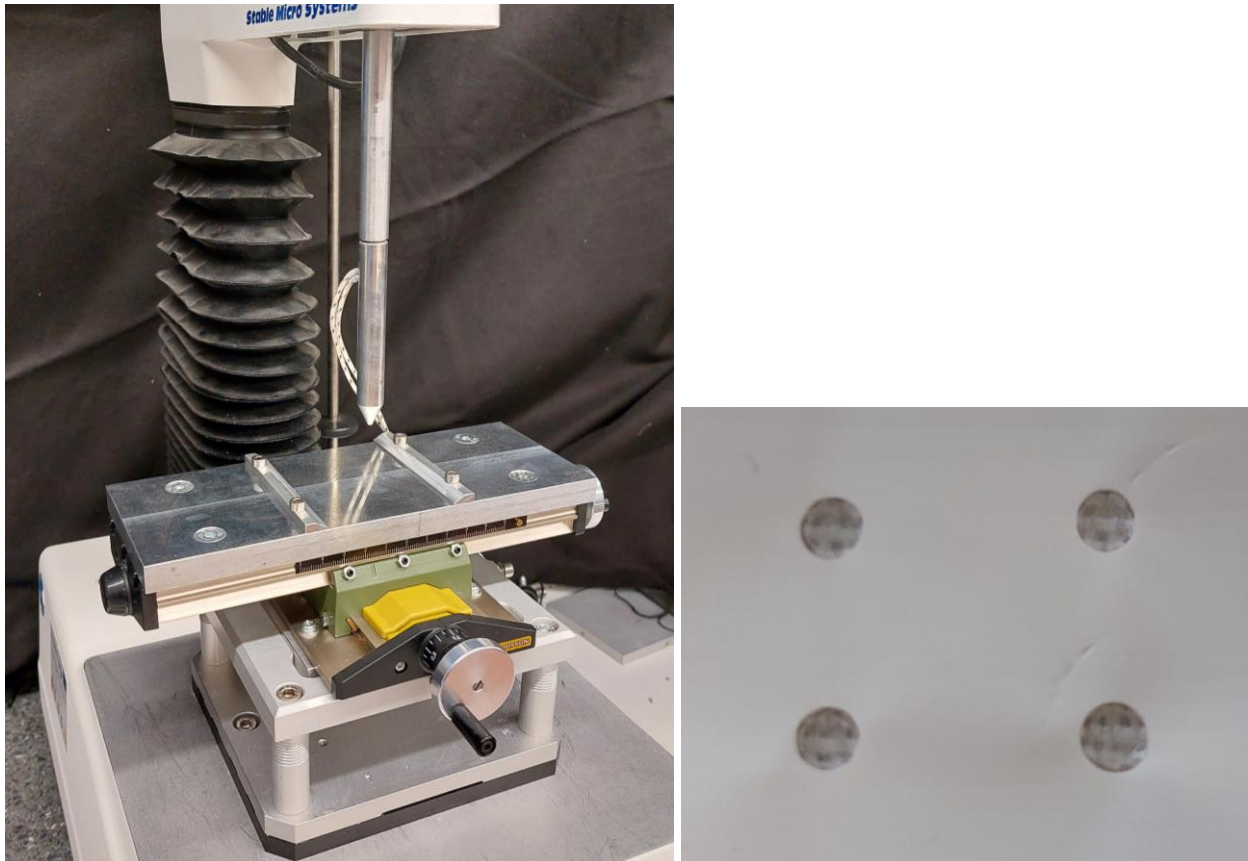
Vorrichtung zur Punktschweißung (links), einzelne Schweißpunkte (rechts)
